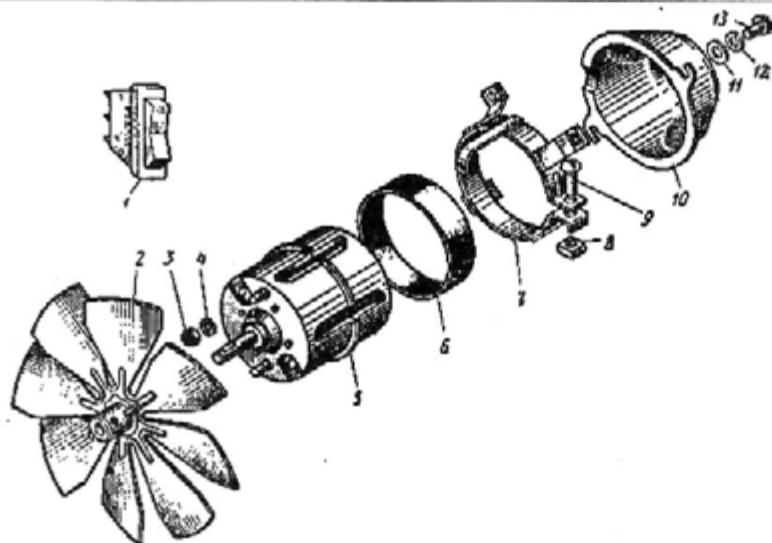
Вентилятор с электродвигателем отопителя кузова и обогревателя ветрового стекла
